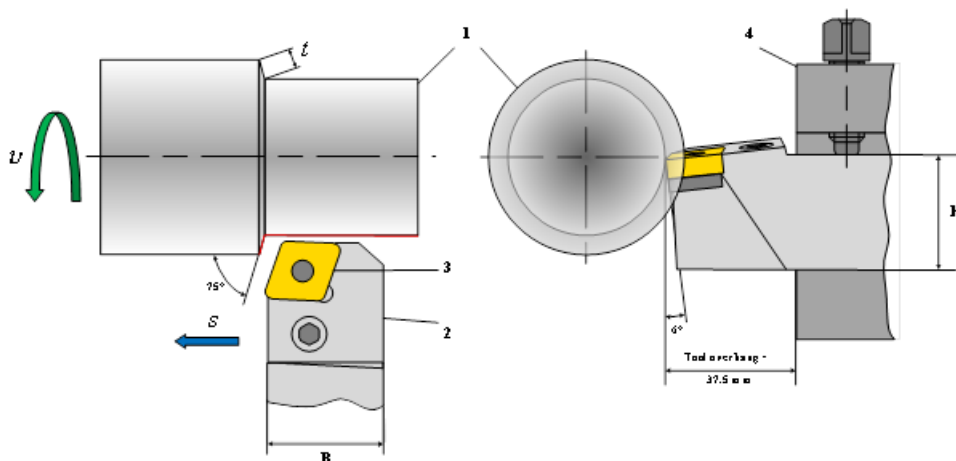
Схема обробки деталі: 1 – Деталь, яка обробляється; 2 – різальний інструмент (PCBNP-4040S-19), 3 – ріжуча вставка (CNMG 190616); 4 – тримач інструменту
